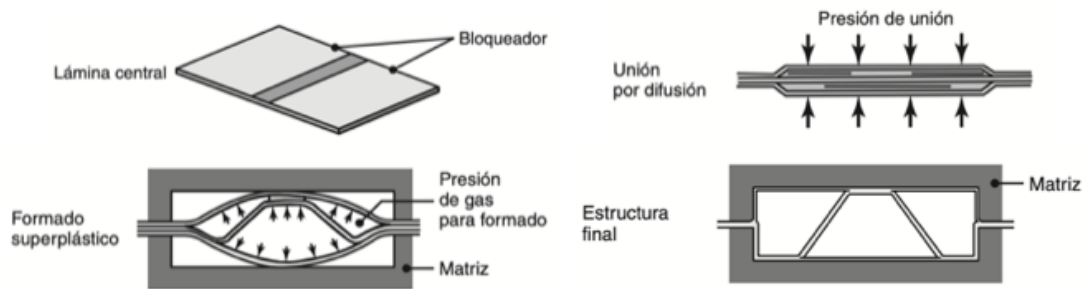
Proceso de soldadura por difusión. [26]
